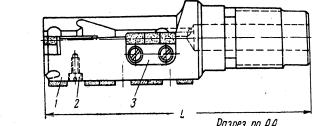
Схема наладки токарного станка для скоростного развертывания цилиндров.
